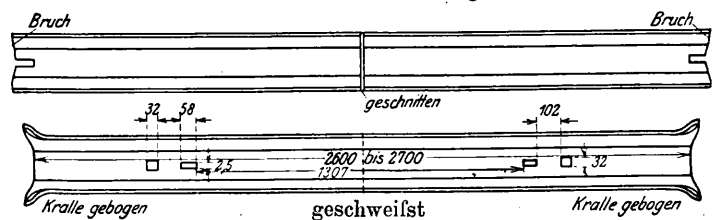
Schmelzschweißung eiserner Querschwellen.
